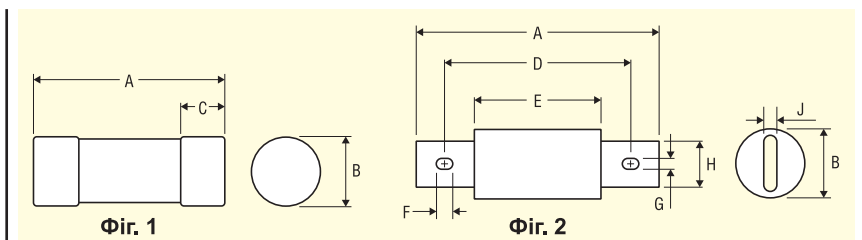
Корпуси, в яких виготовляються запобіжники серії LDFJ
